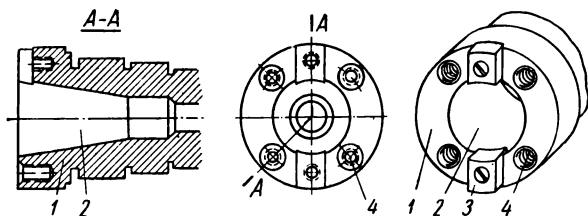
Передний конец шпинделя отечественных фрезерных станков
